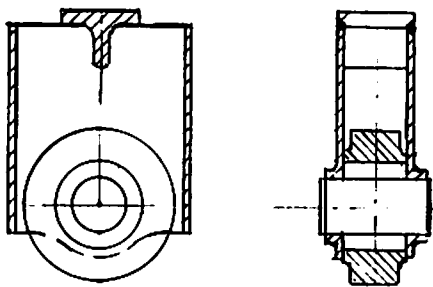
Kastenstößel mit Rolle – ergibt kurze Baulänge.
